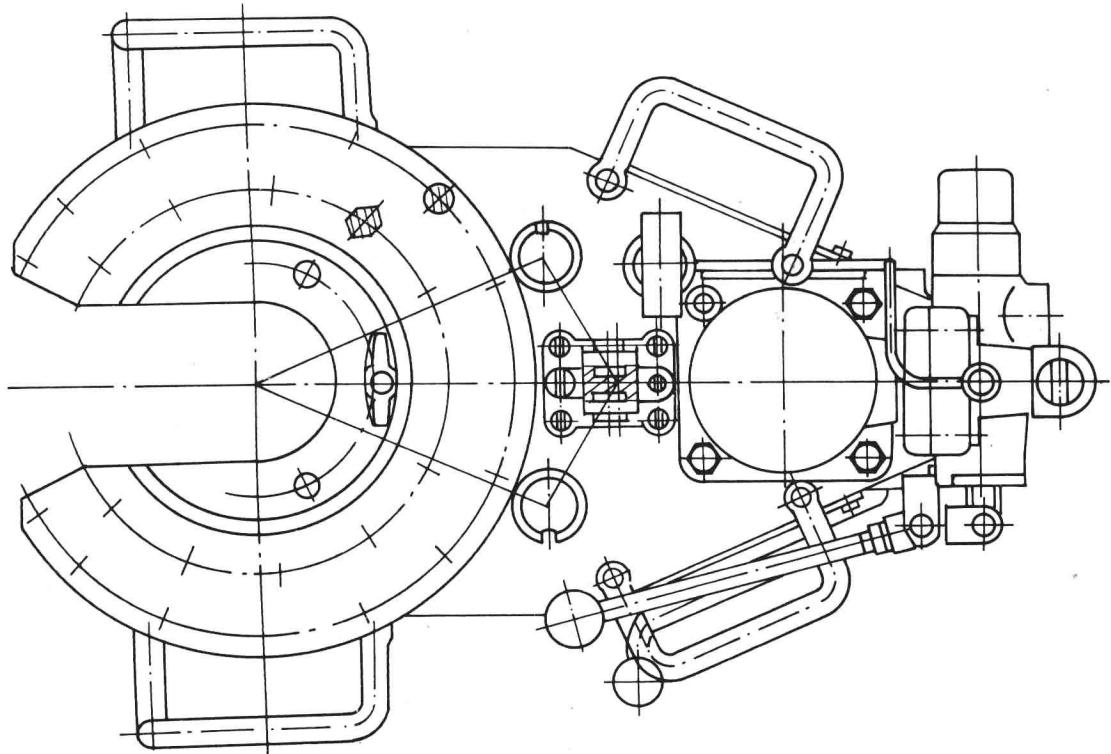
XYQ3B 型液压油管钳主钳俯视图
